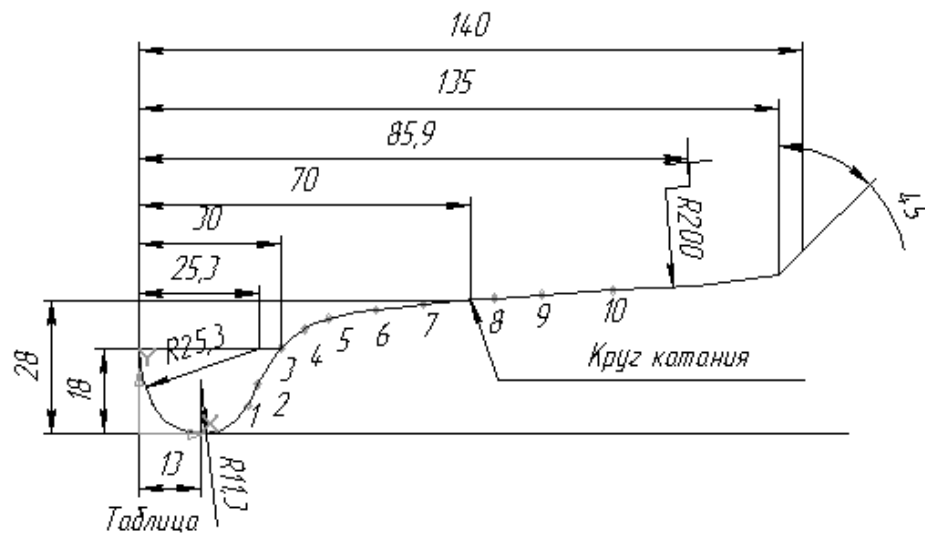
Схема настройки фасонных фрез для станка КЖ-20
